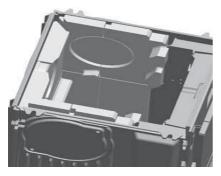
Pose des pierres latérales avant haut droite (H2.1-15) et avant haut gauche (H2.1-17).
